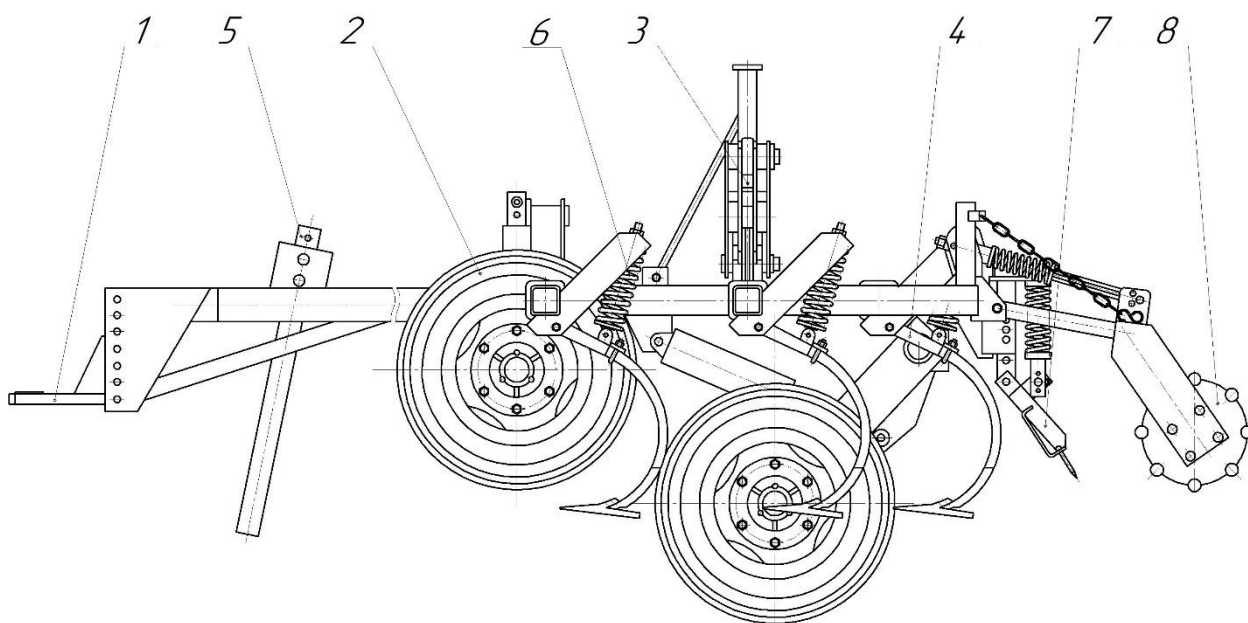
Схема культиватора КШУ 8 для передпосівного обробітку ґрунту:
